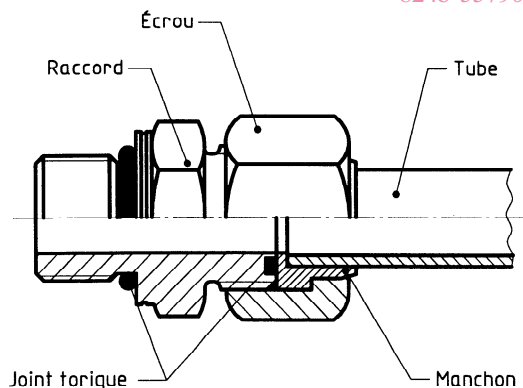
Coupe transversale d'un raccord type à joints faciaux toriques
